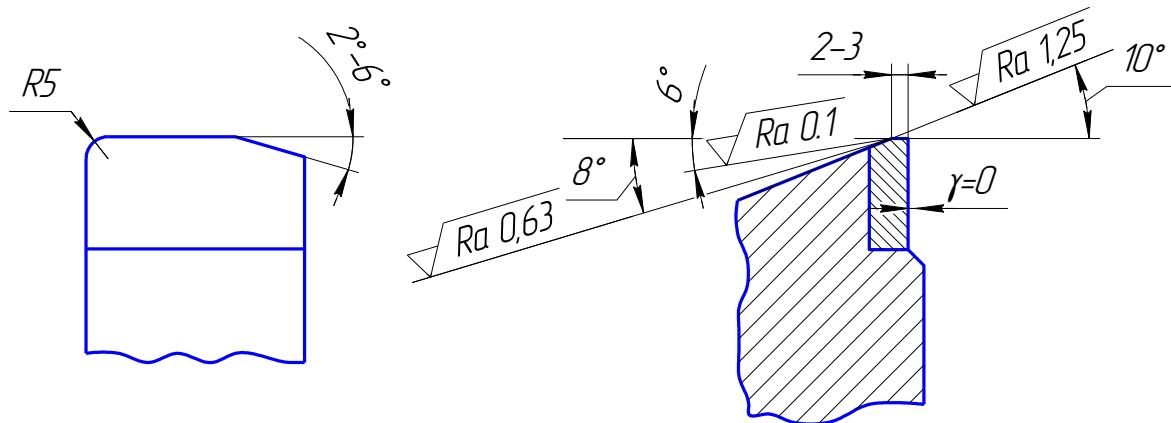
Стругальний різець для чистової обробки площин
